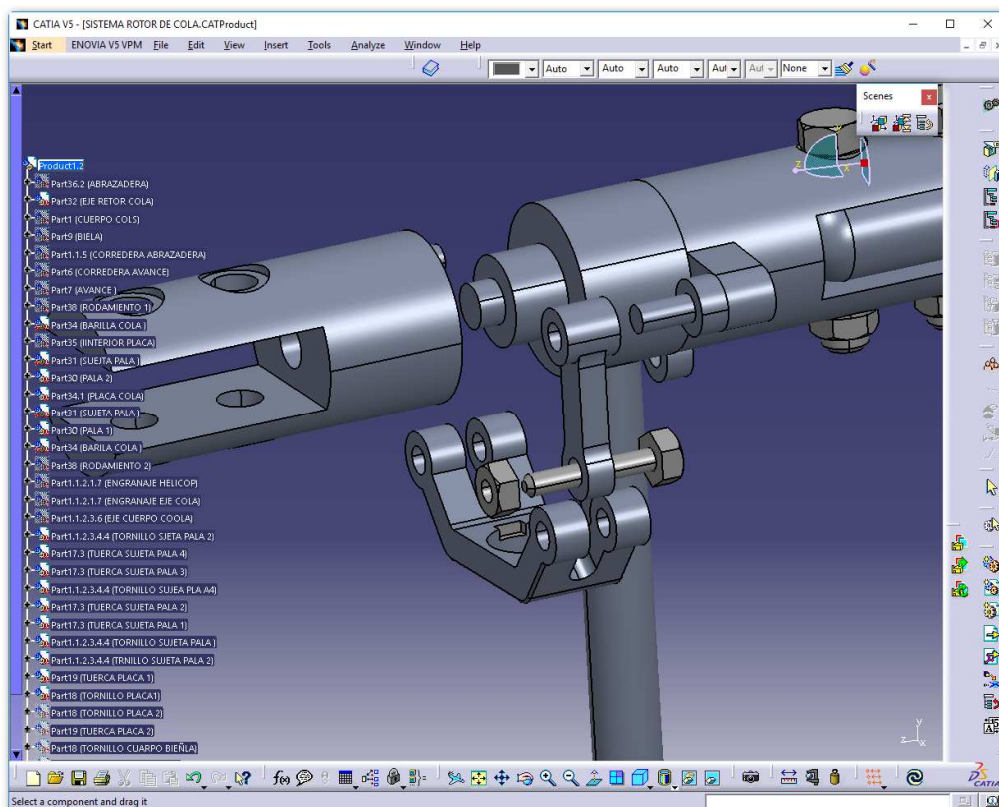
Unión placa y barra con el eje del rotor de cola.
